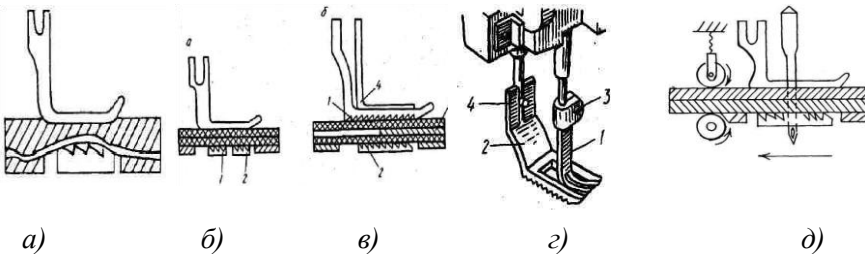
Види механізмів просування матеріалів: а) – однорейковий, б) – диференційний, в),–двухрейковий з верхньою і нижньою рейками (1-верхня рейка, 2- нижня рейка, 3 – розподілююча пластинка, 4-лапка; г) – взаєморозташування лапки з верхньою рейкою (1-лапка. 2-верхня рейка, 3,4 –гвинти кріплення); д) – комбінований.
